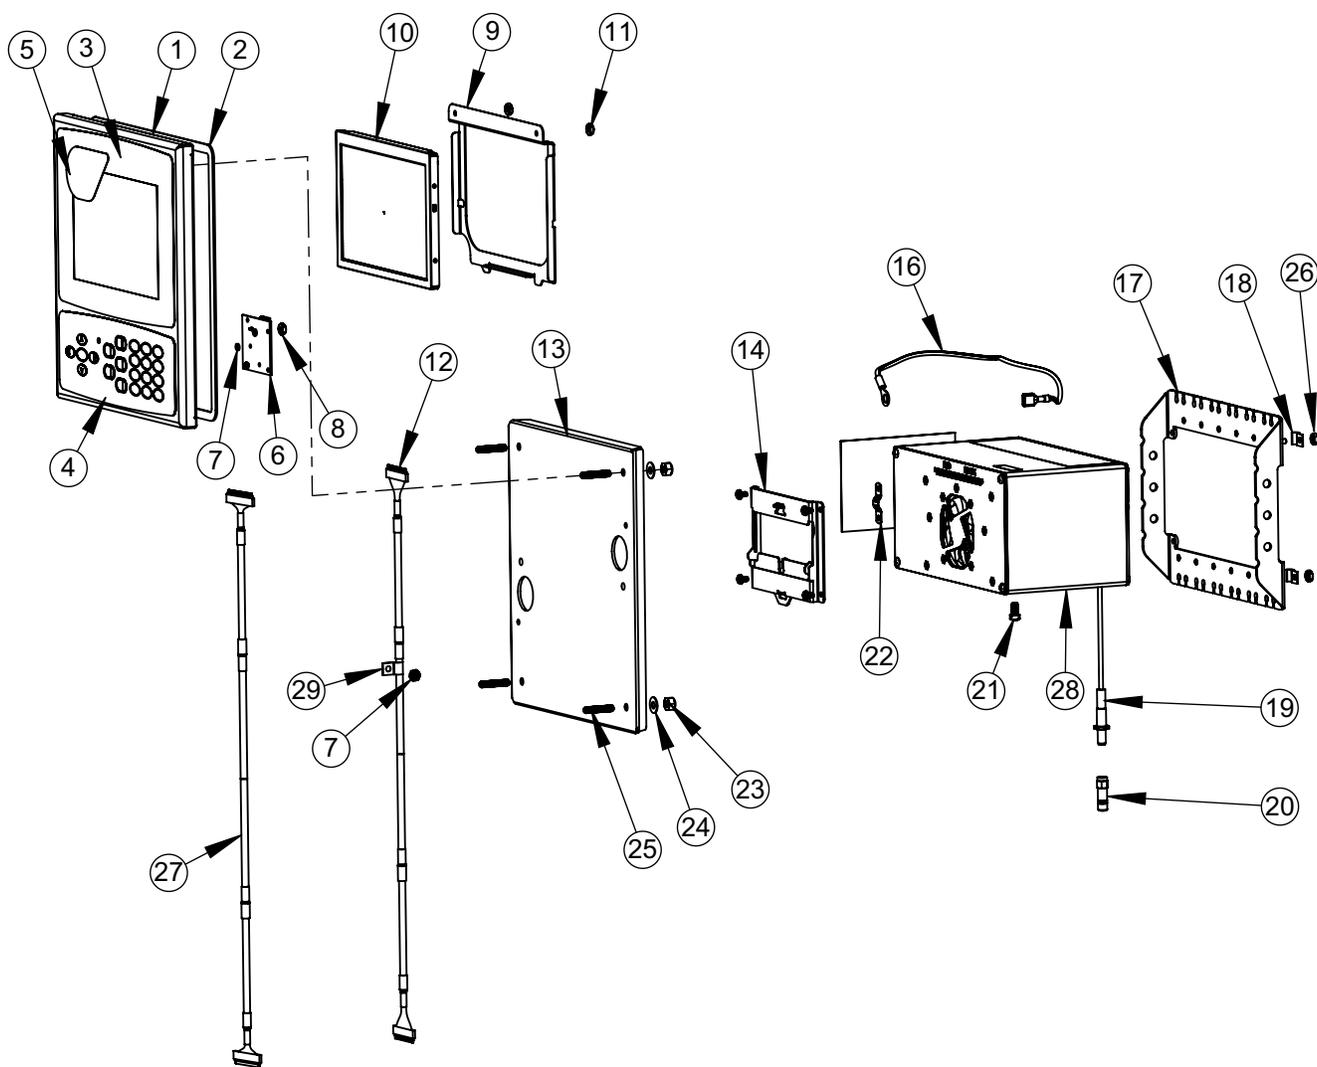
Componenti per la riparazione dell'indicatore da 7" con montaggio a pannello
